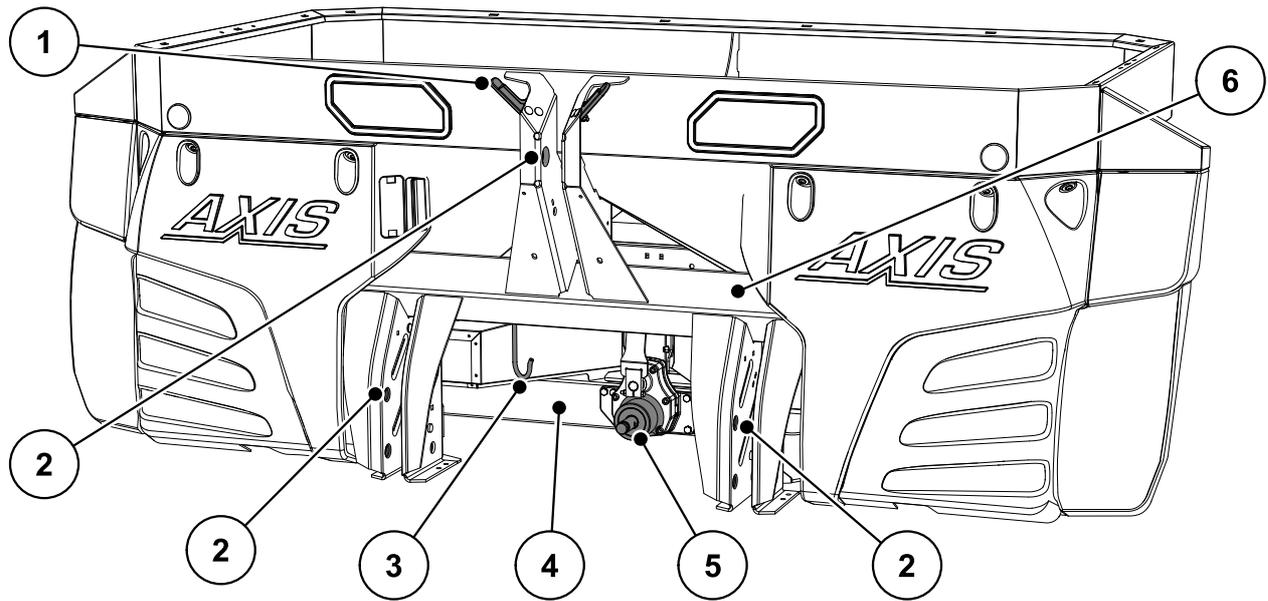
Aperçu des composants : exemple AXIS 30.1 - vue avant
